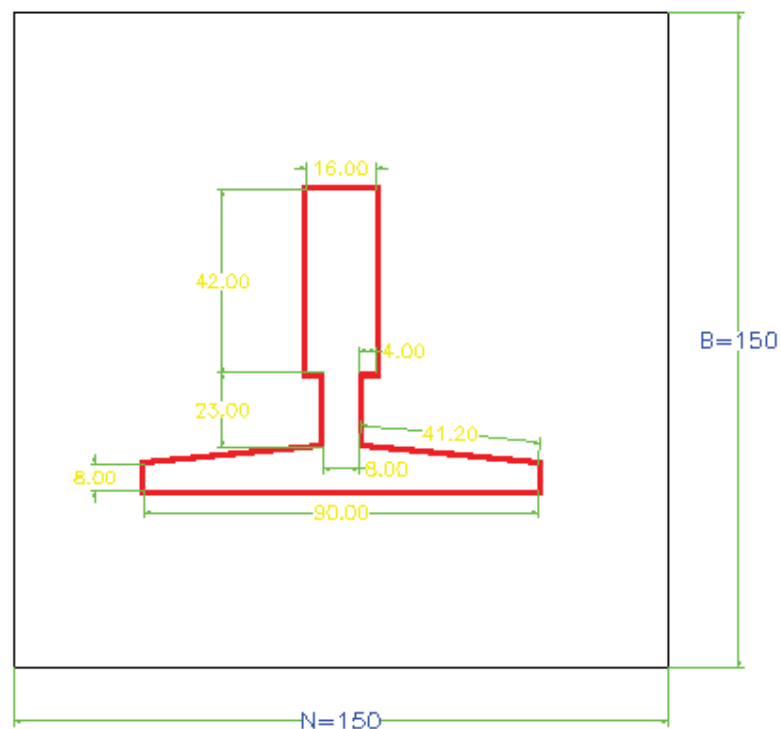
28 Junta de soldadura entre guía y placa base
